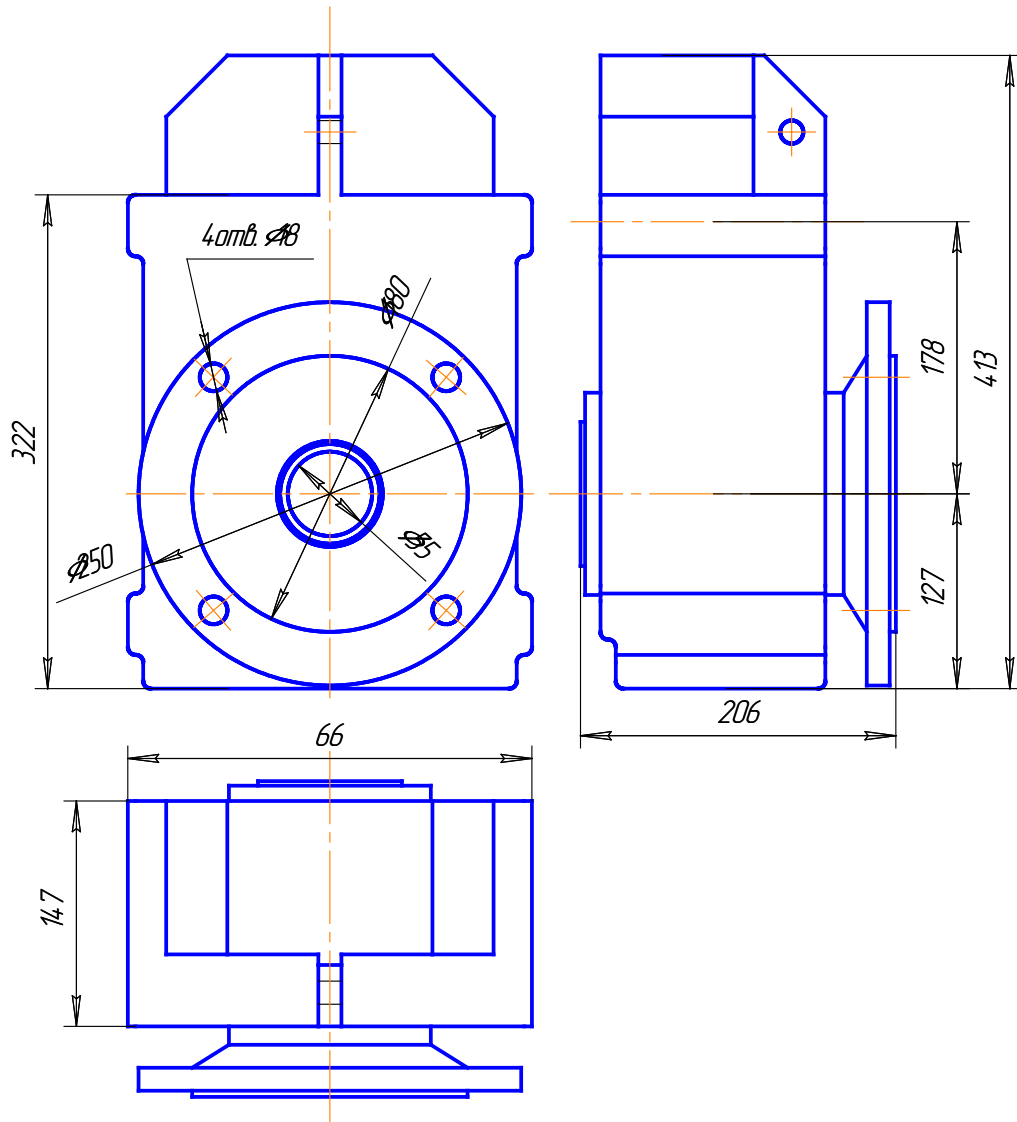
Ескіз редуктора типу ВА F298 EN 0.300 фірми «Flender»,
